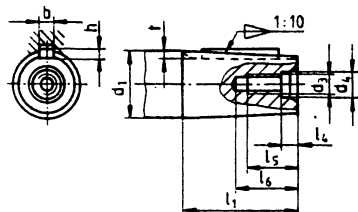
Kegelige Wellenenden mit Innengewinde
